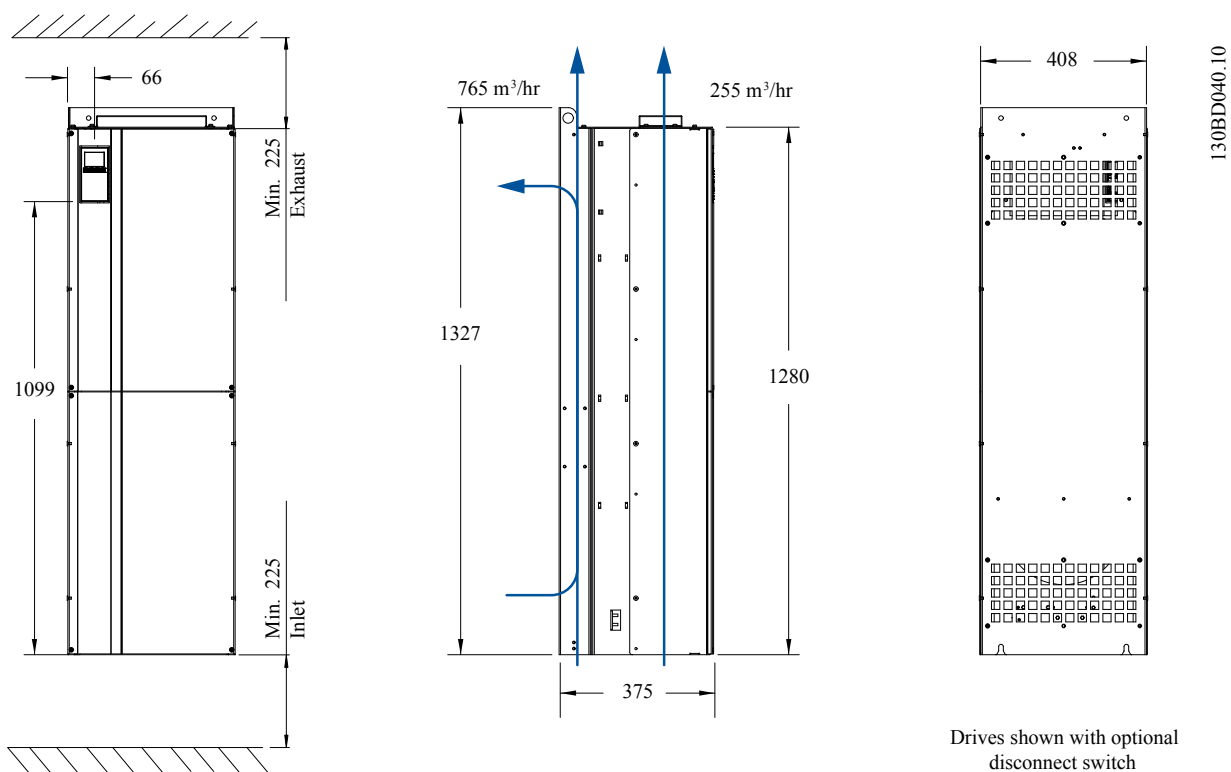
Gerätegröße 44 (Schaltschrankbefestigung)
